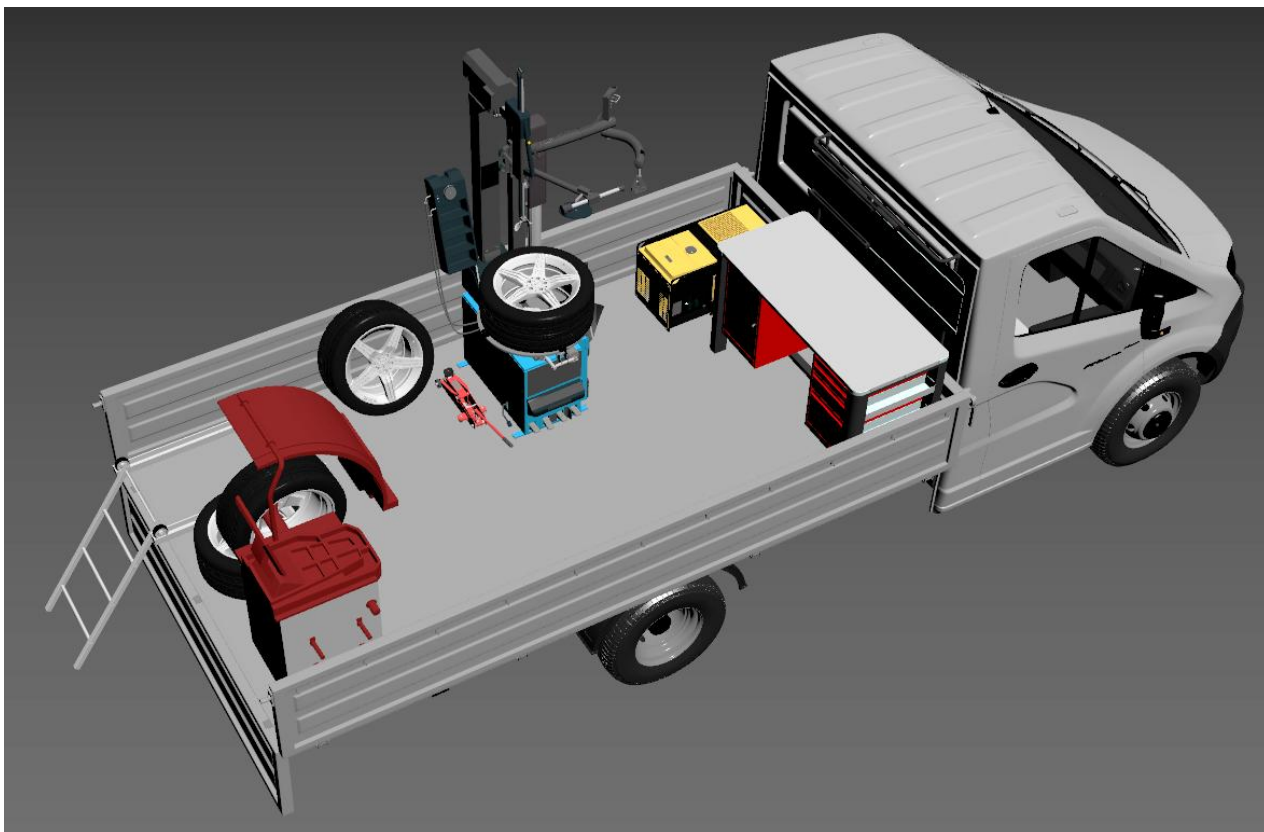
Компоновка мобильного шиномонтажного комплекса на базе бортового автомобиля Газель Next (A21R23-10)
